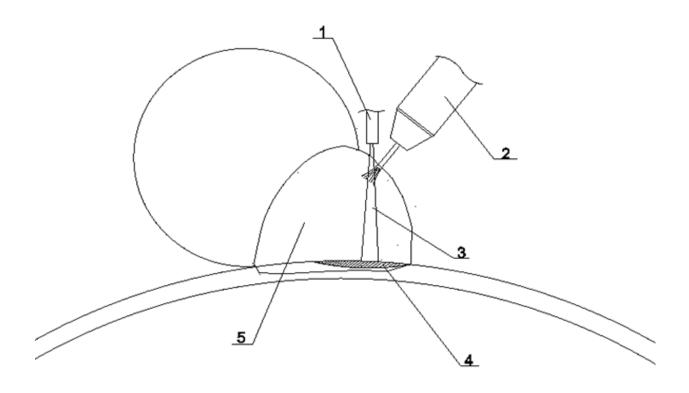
Принципиальная схема гибридной сварки с последовательным расположением источников нагрева
